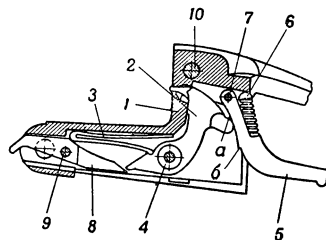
Коленчатая колодка дробового двуствольного ружья, модель ИЖ-49, с ударными механизмами, расположенными внутри корпуса коробки до модернизации:
